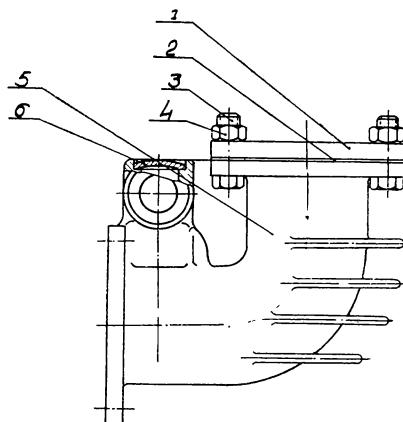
Порядок затяжки гаек крышки цилиндров.
